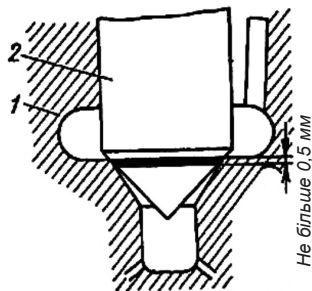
Притиральний поясок корпусу розпилювача та голки форсунки:
